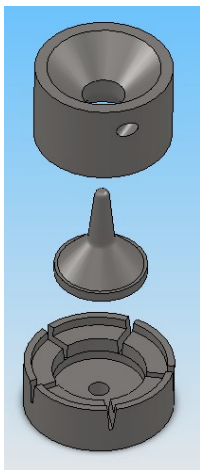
Vista explodida, em projeção dimétrica, dos componentes do novo molde.
